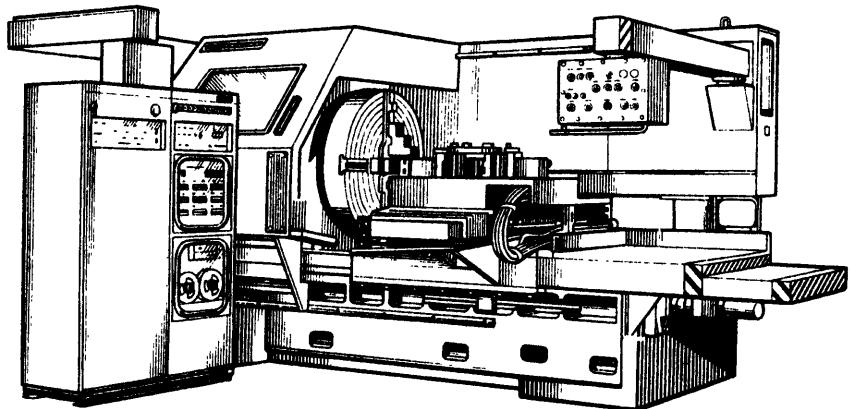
Токарный специальный патронный станок повышенной точности модели МК6713С5 с ЧПУ
